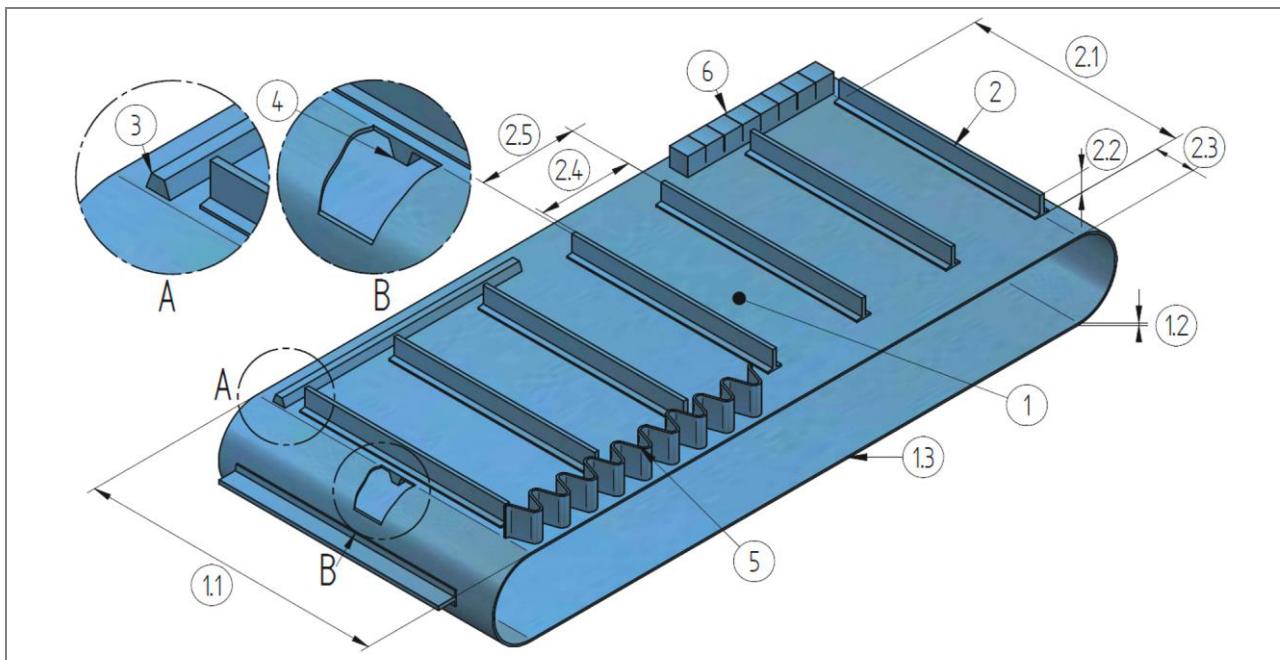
Explosivní náhled rovného pásového dopravníku (příklad)
